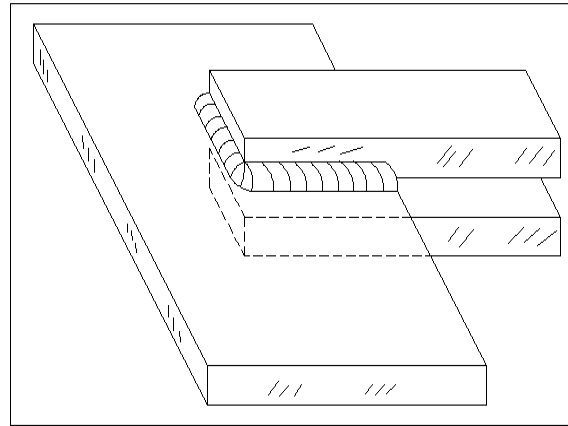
Detalle estructural de doble placa soldada. Ref. [30]
